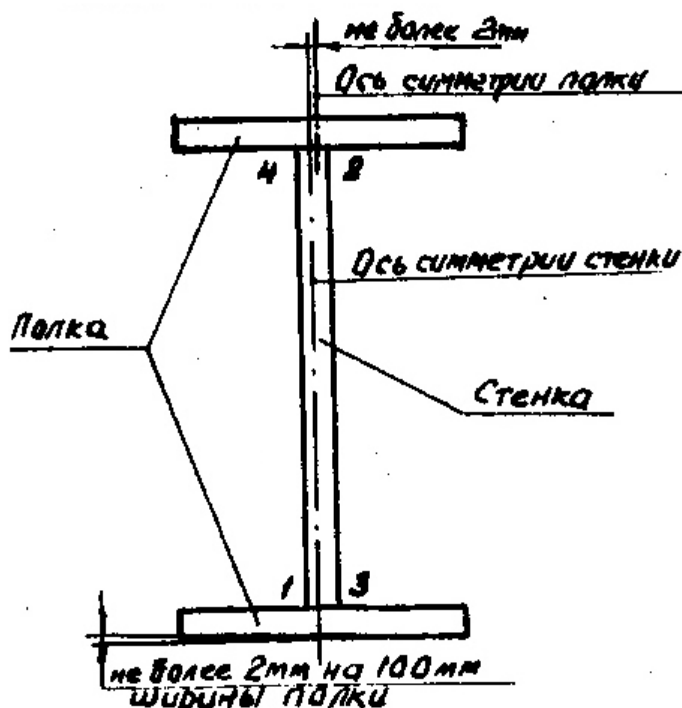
Технические требования к точности изготовления двутавровой балки: 1...4 – номера сварочных швов.
